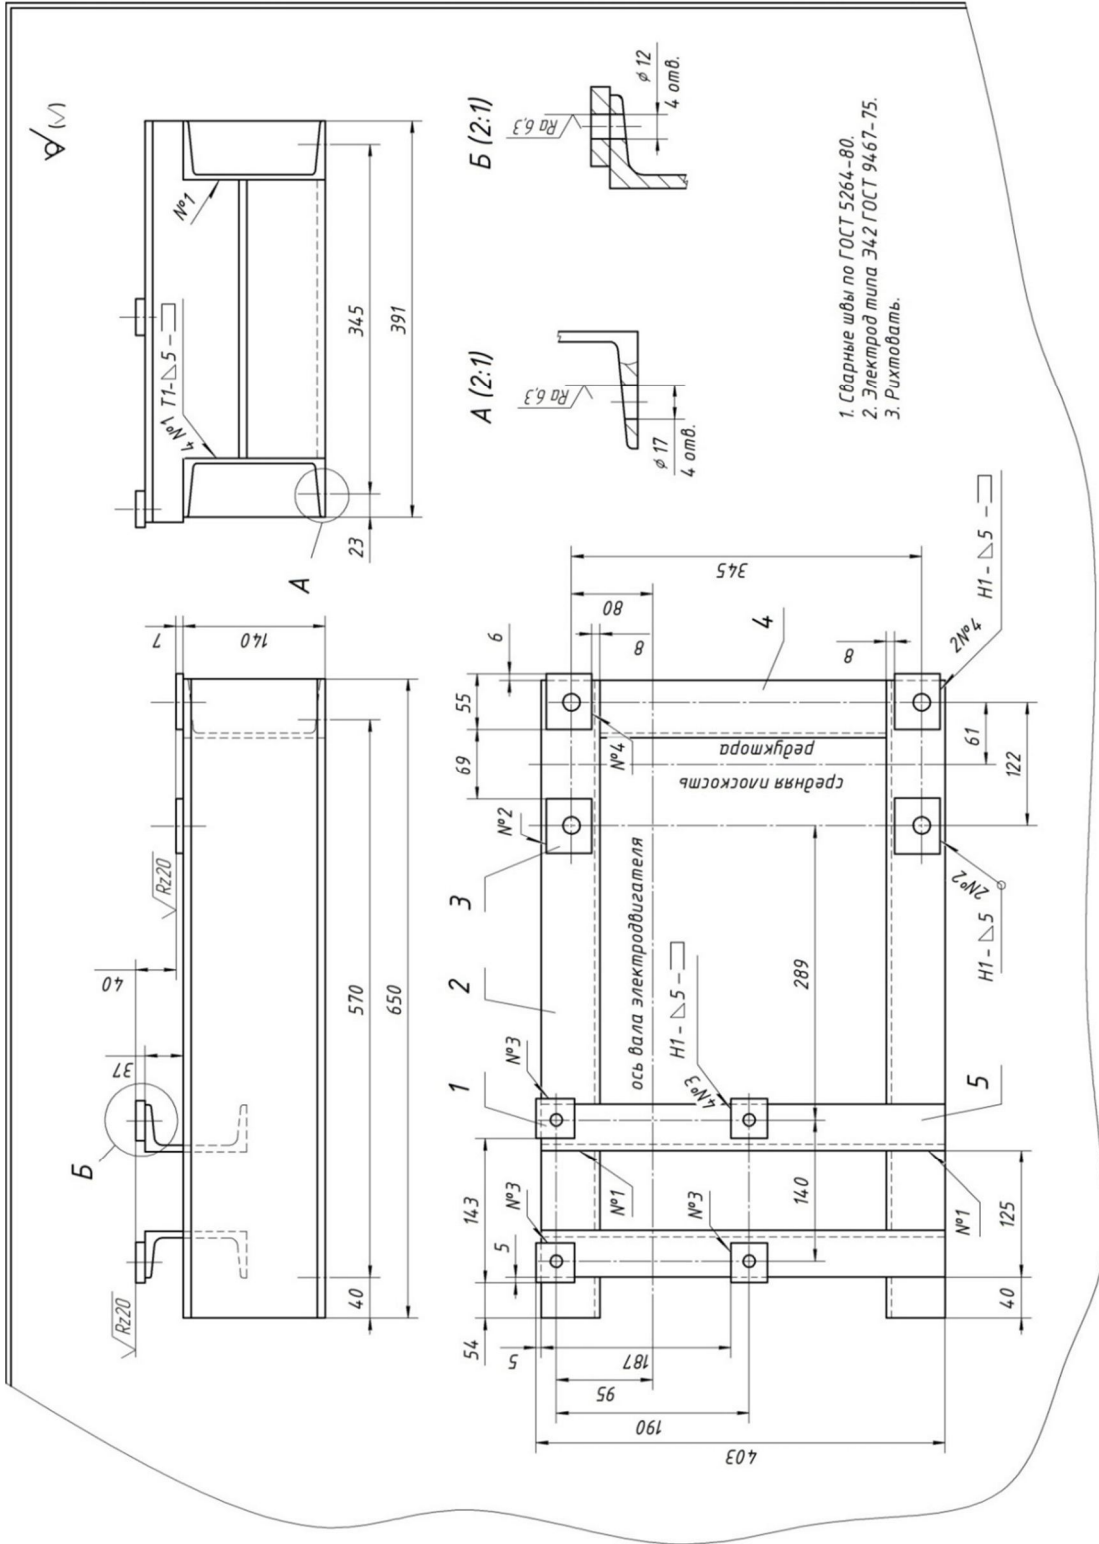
Пример чертежа сварной рамы привода
